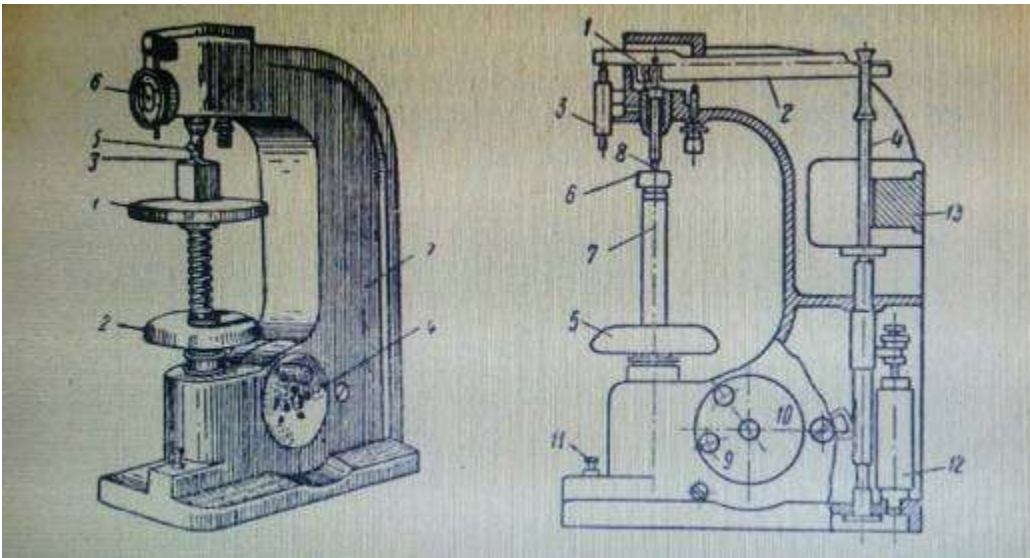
А-прибор Роквелла: 1-подставка, 2-маховик,3-алмазный конус, 4-рукоятка, 5-наконечник, 6-индикатор,7-станина;
